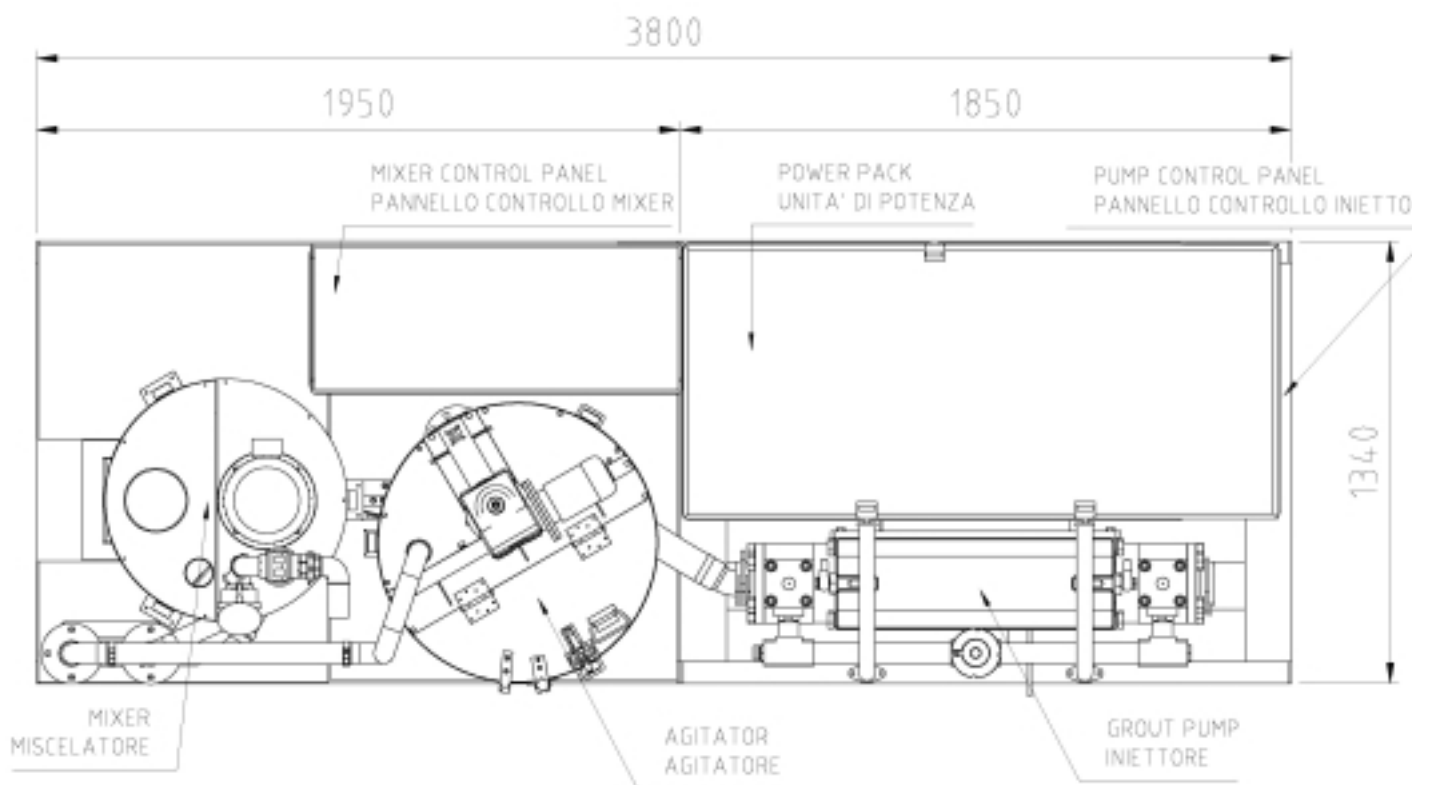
"MINIJET" COMPACT UNIT - schema planimetrico / *planimetric scheme.
